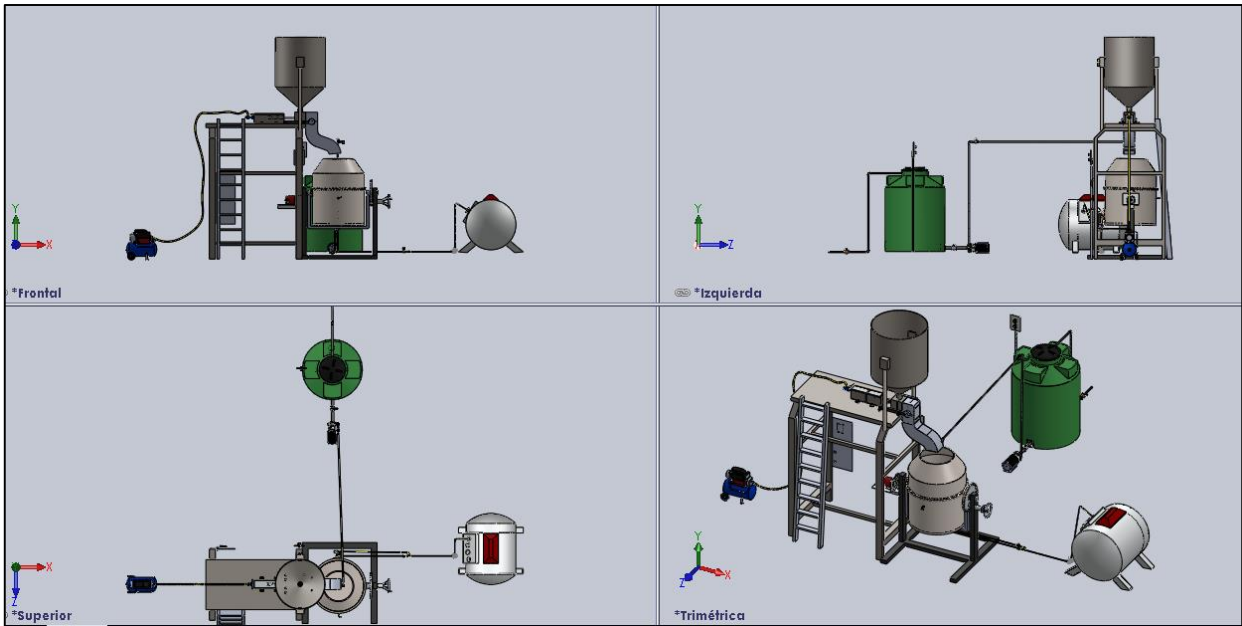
Vistas frontal, izquierda, superior y trimétrica.
